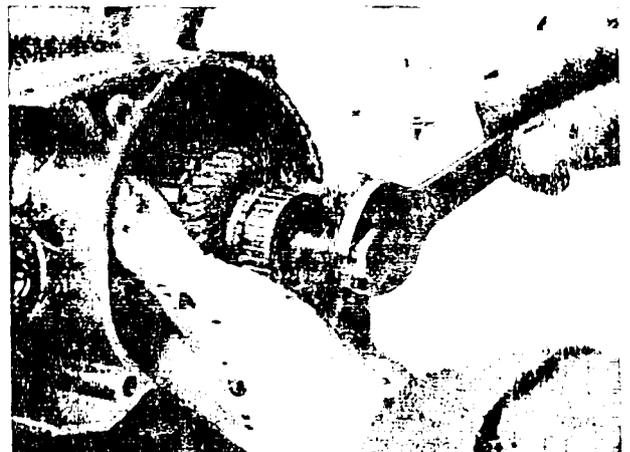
Abdrücken des Ankers RT 125 mittels Abdruckschraube Nr. 0100027
